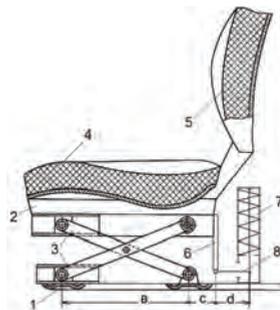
б. Общий вид подвески сиденья с направляющим механизмом типа «ножницы».
